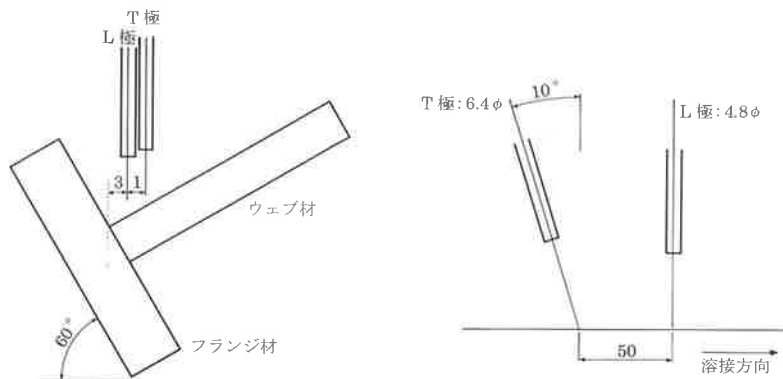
2電極サブマージアーク溶接の電極配置図
